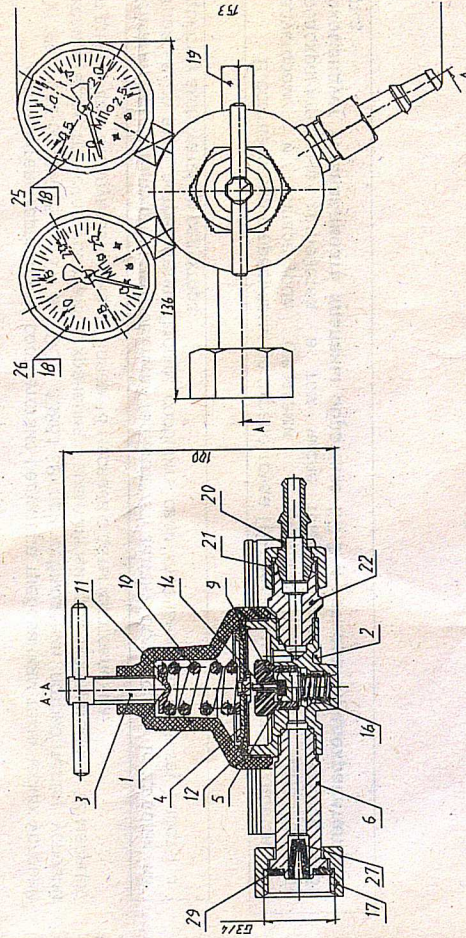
Редуктор баллонный кислородный одноступенчатый.
